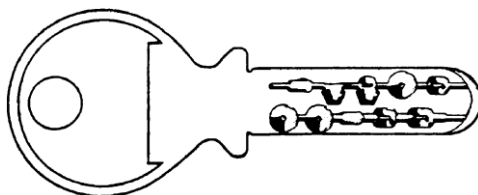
Луночный ключ с углублениями, выполненными сверлом или фрезой
